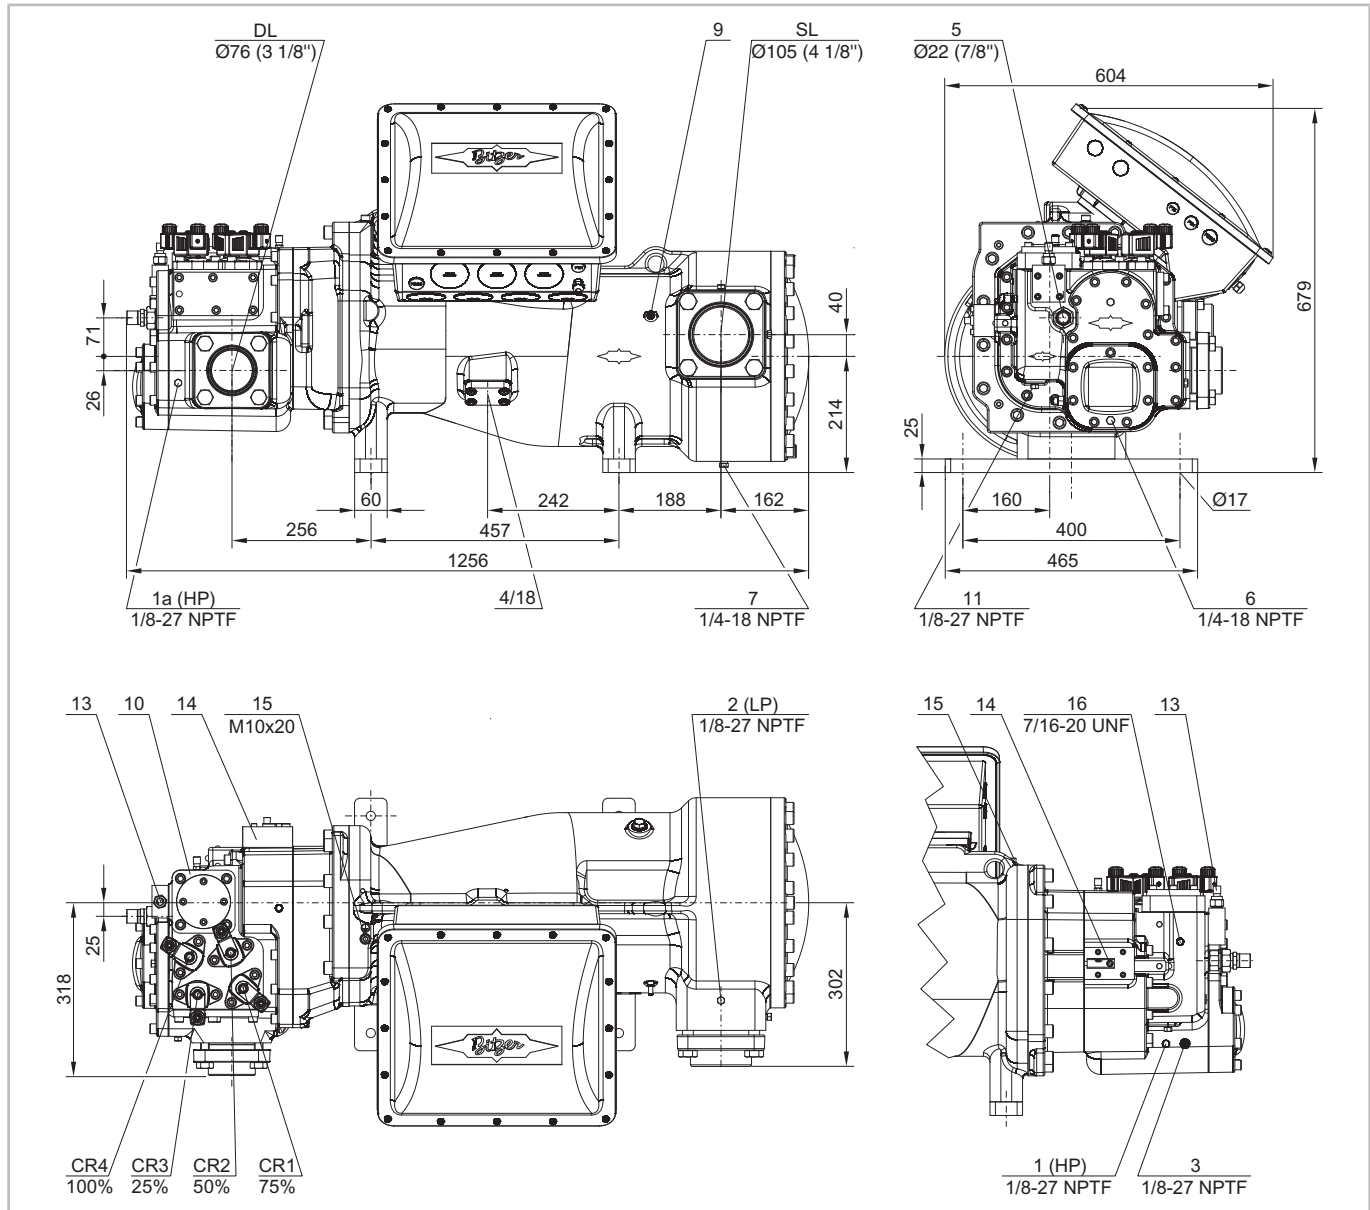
Maßzeichnung HS.8551 .. HS.8571
